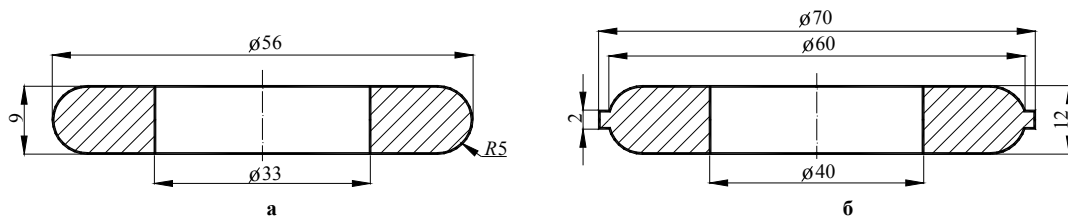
Ролик (а) і заготовка ролика до спікання (б)
